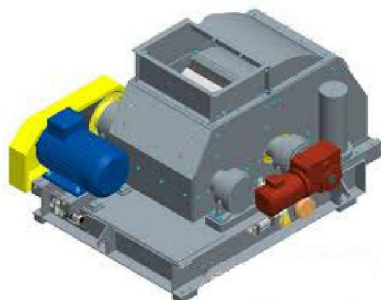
Загальний вид валкових дробарок серії PL 600
